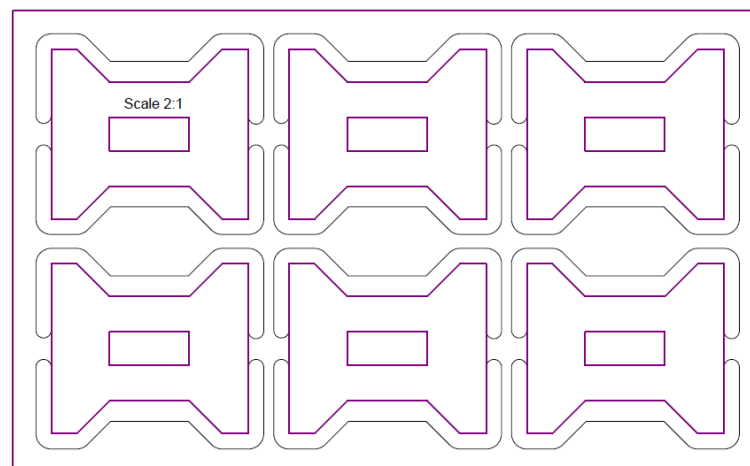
layer stack legend e disegno del PCB per la realizzazione degli avvolgimenti.
